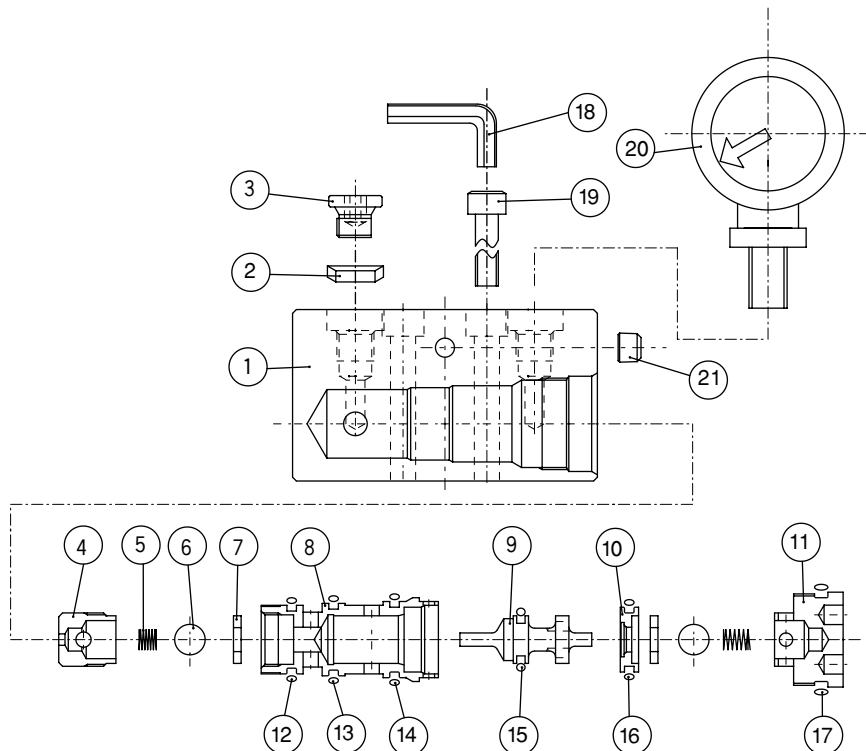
標準ブロックを外した状態 With the standard block removed
